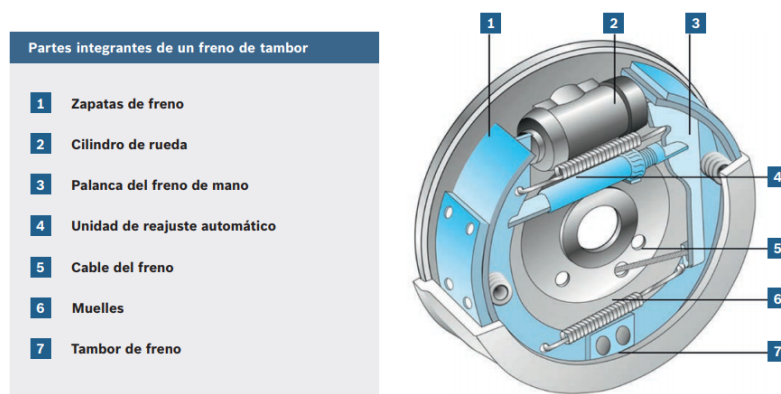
Ficha Técnica: Frenos de Tambor de Bosch. Tomado de Bosch, 2017 [9].
